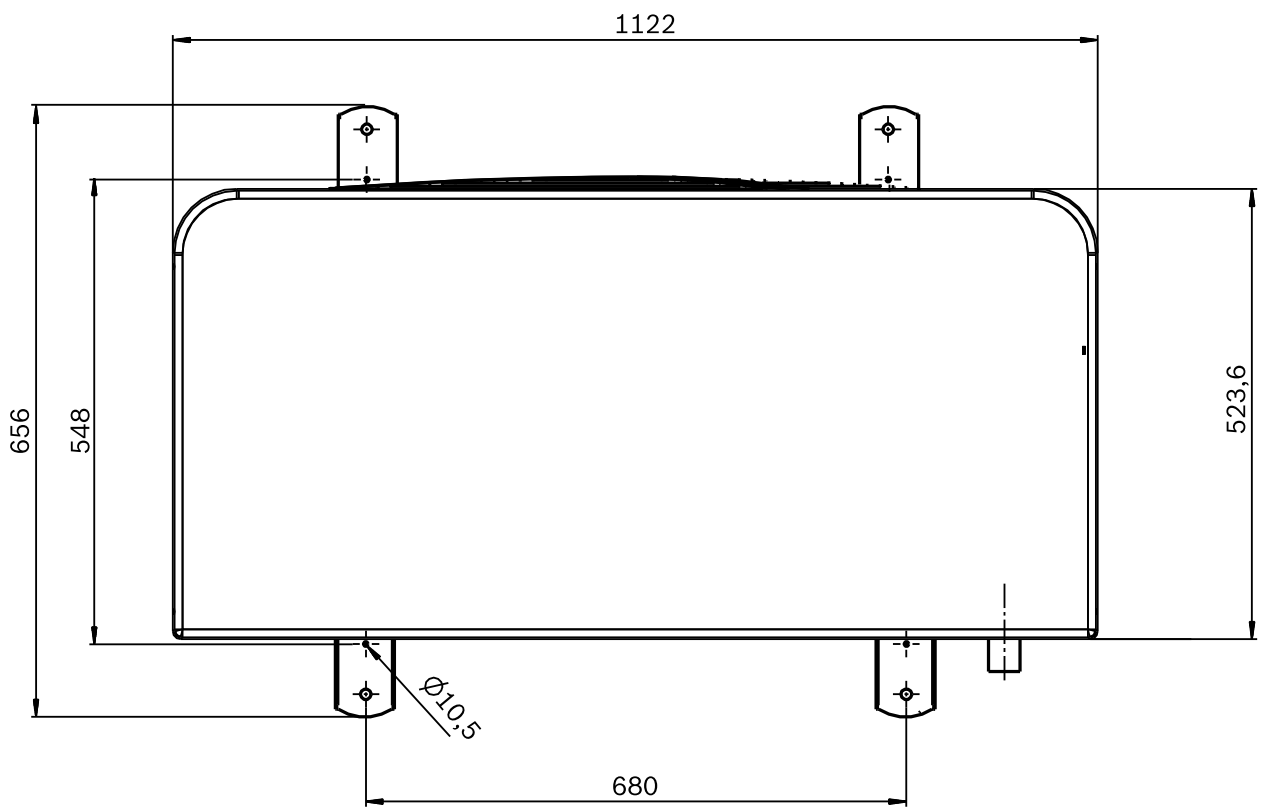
Dimensiones de SAO40-2, SAO60-2, SAO80-2, vista en planta
